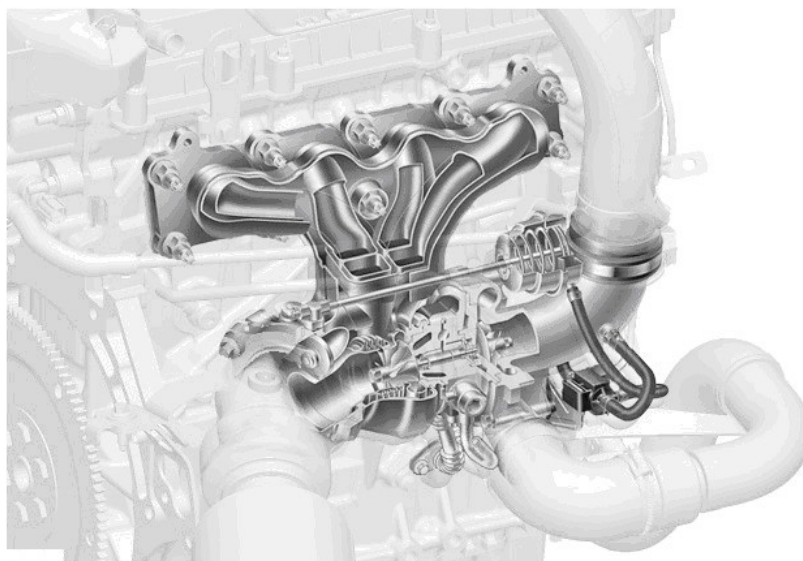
Сегмент коллектора и турбокомпрессора бензинового двигателя 2.0L GTDi
